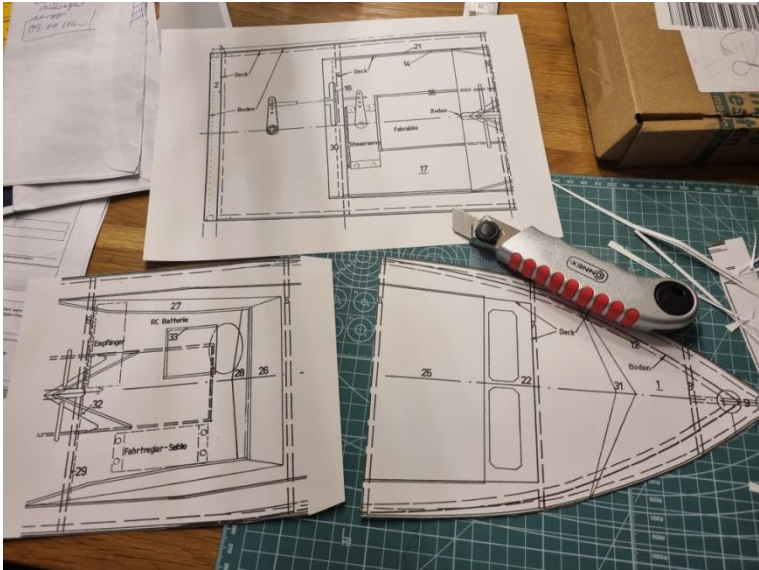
Alle drei Decksteile, teilweise zugeschnitten
